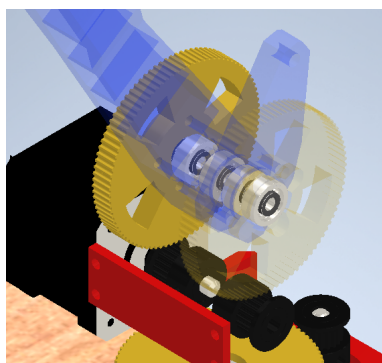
Rodamientos incluidos en la parte media del cuerpo del robot.
